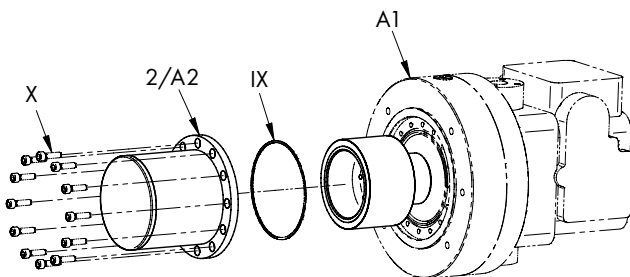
Prinzipielle Spaltpfopfmontage/-abdichtung an einem Flansch für technisch dichte Systeme (A4)
